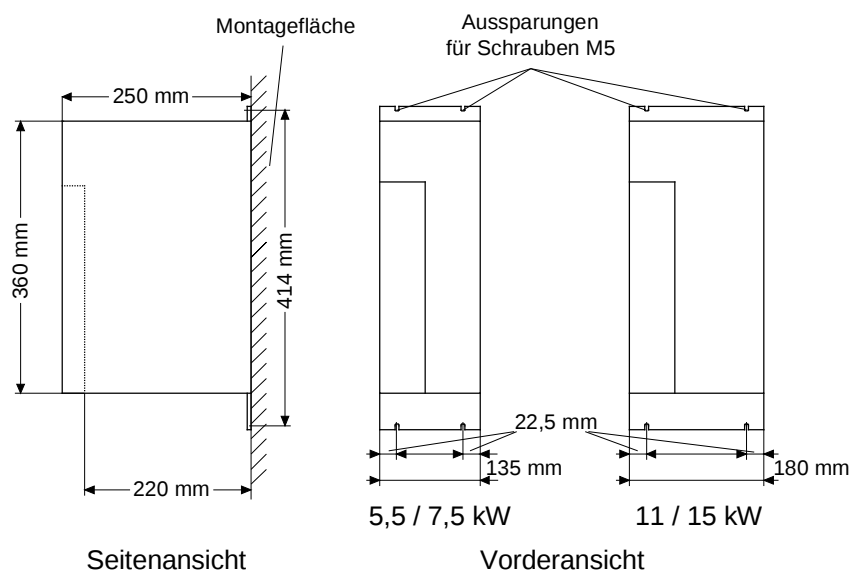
Maßbilder für Gehäusebreite 135 mm und 180 mm
